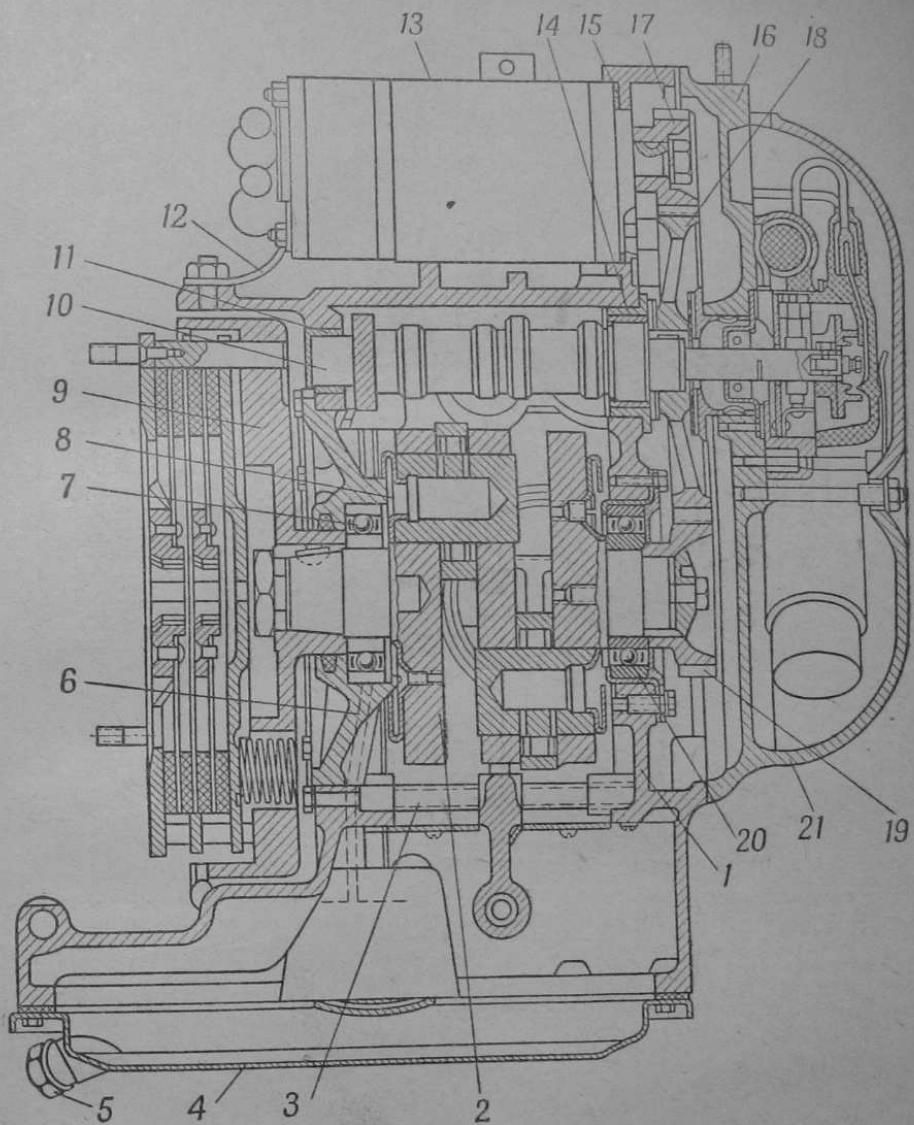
Двигатель мотоцикла М-72. Продольный разрез:
